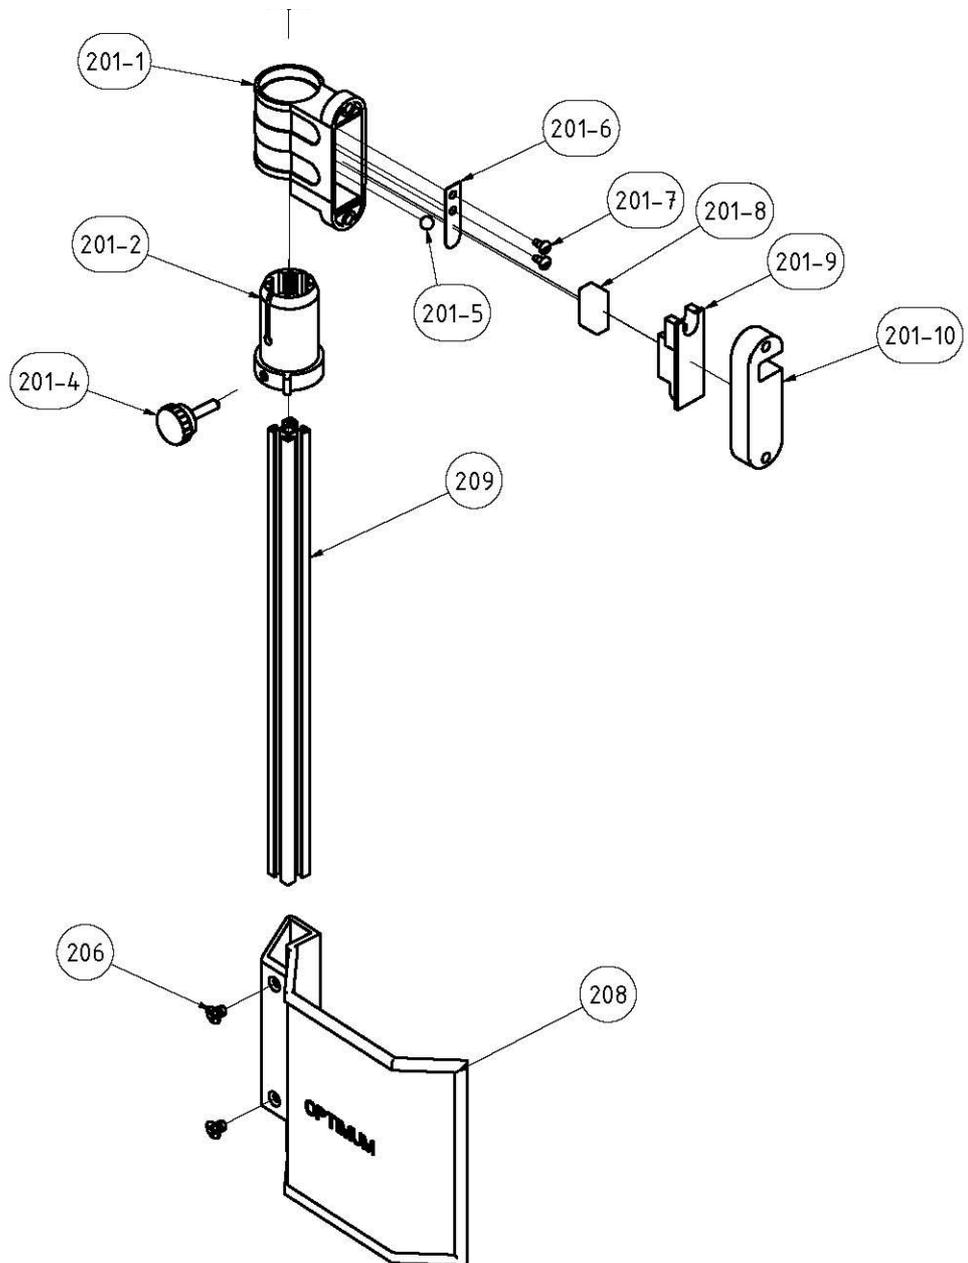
Bohrfutterschutz B23 Pro ; B26 Pro - Drill chuck protection B23 Pro ; B26 Pro
